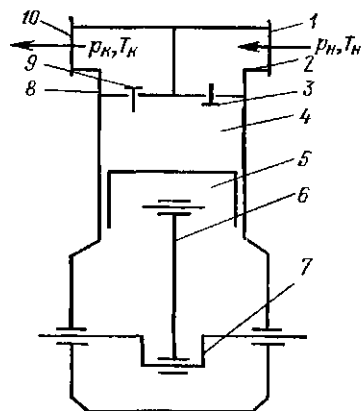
Схема поршневого компрессора с одной рабочей камерой и тронковым поршнем:
